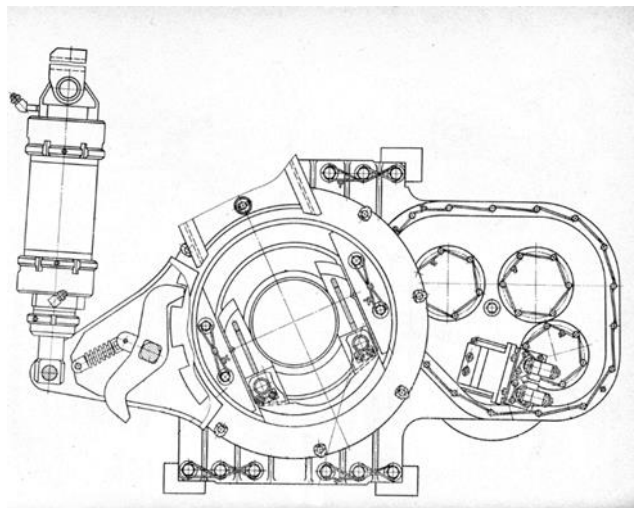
Механізм з'єднання та роз'єднання штанг
